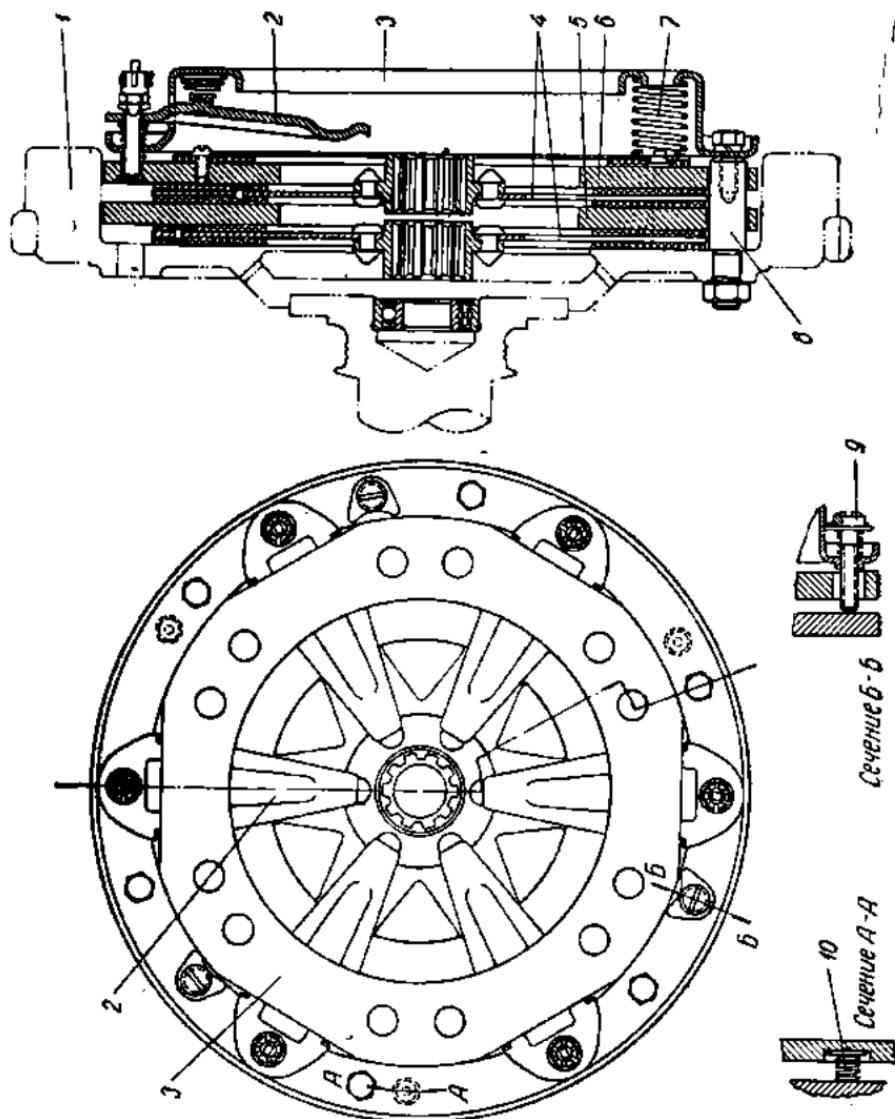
Сцепление. (1 — маховик; 2 — выжимной рычаг; 3 — кожух сцепления; 4 — ведомые диски; 5 — средний ведущий диск; 6 — второй ведущий диск; 7 — нажимная пружина; 8 — ведущий палец; 9 — установочный винт; 10 — вспомогательная пружинка).
